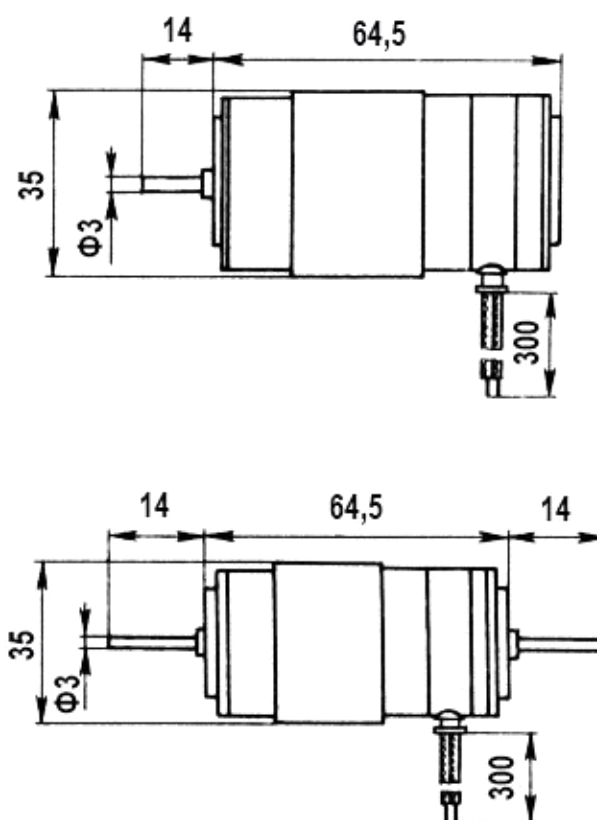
Внешний вид электродвигателей ДПМ-35.
